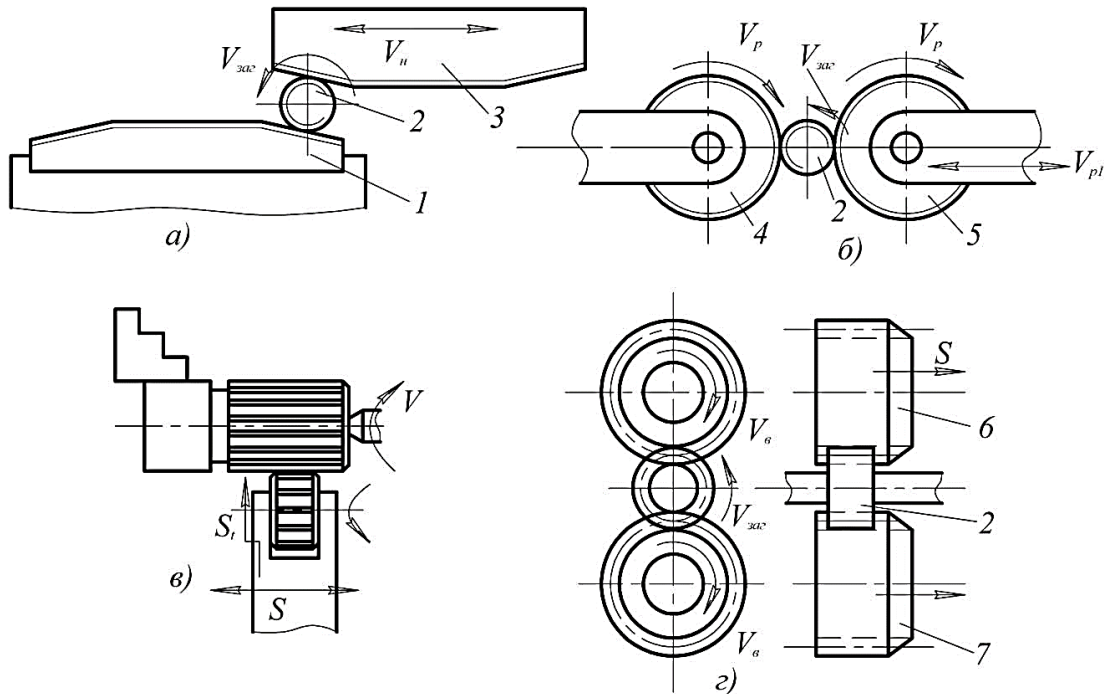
Схеми формуювальних методів обробки пластичним деформуванням
